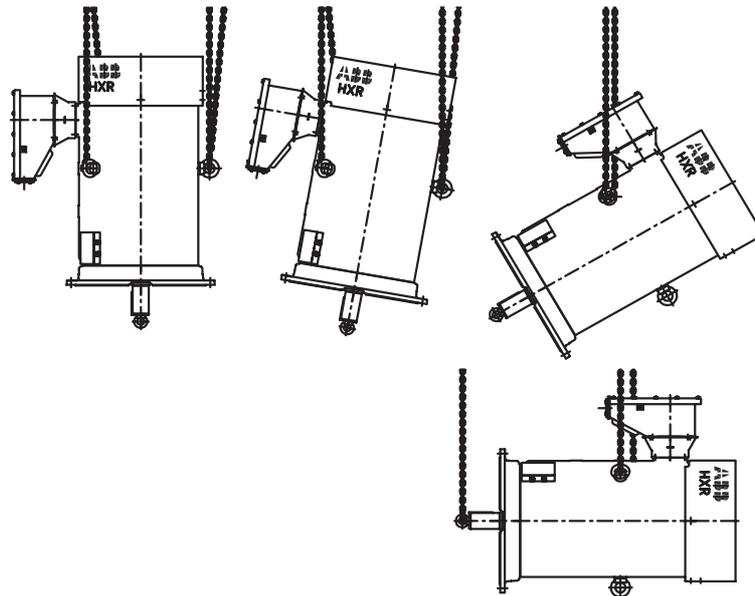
Machine équipée d'anneaux de levage tournants : levage et rotation
